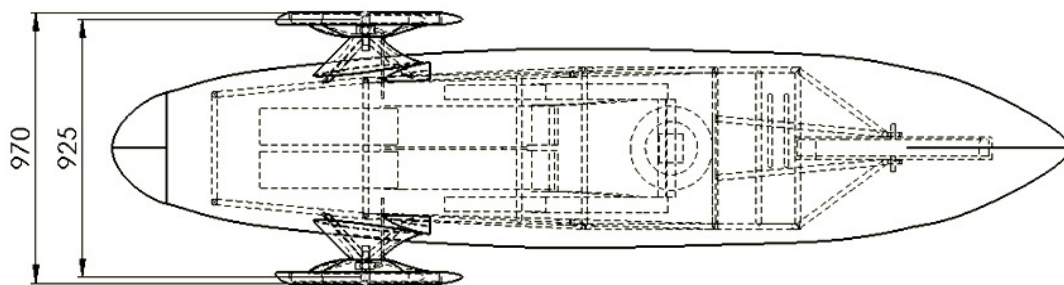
Model vozidla se zúženou zádí s kryty předních kol a jejich zavěšení
